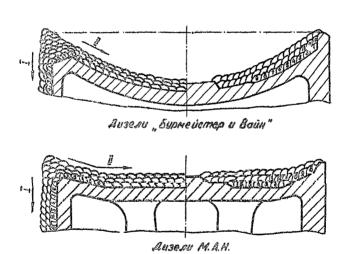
Схомы дуговой налиавки дница и неружной цалиндрической поверхности головки поршня
